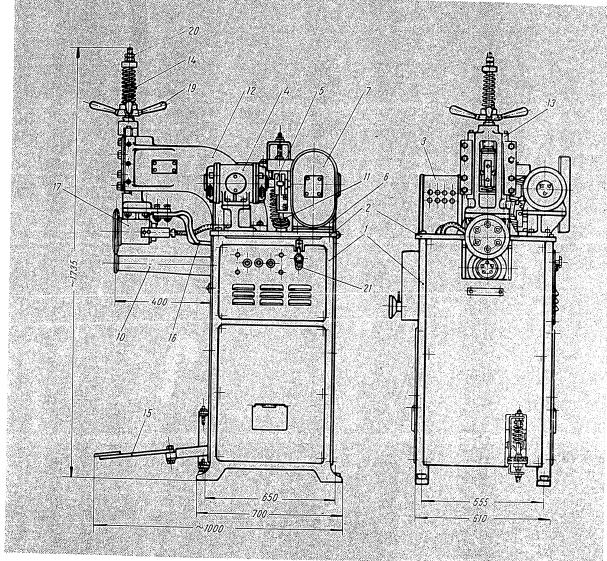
Устройство машины МШМ-50 для поперечной сварки.
